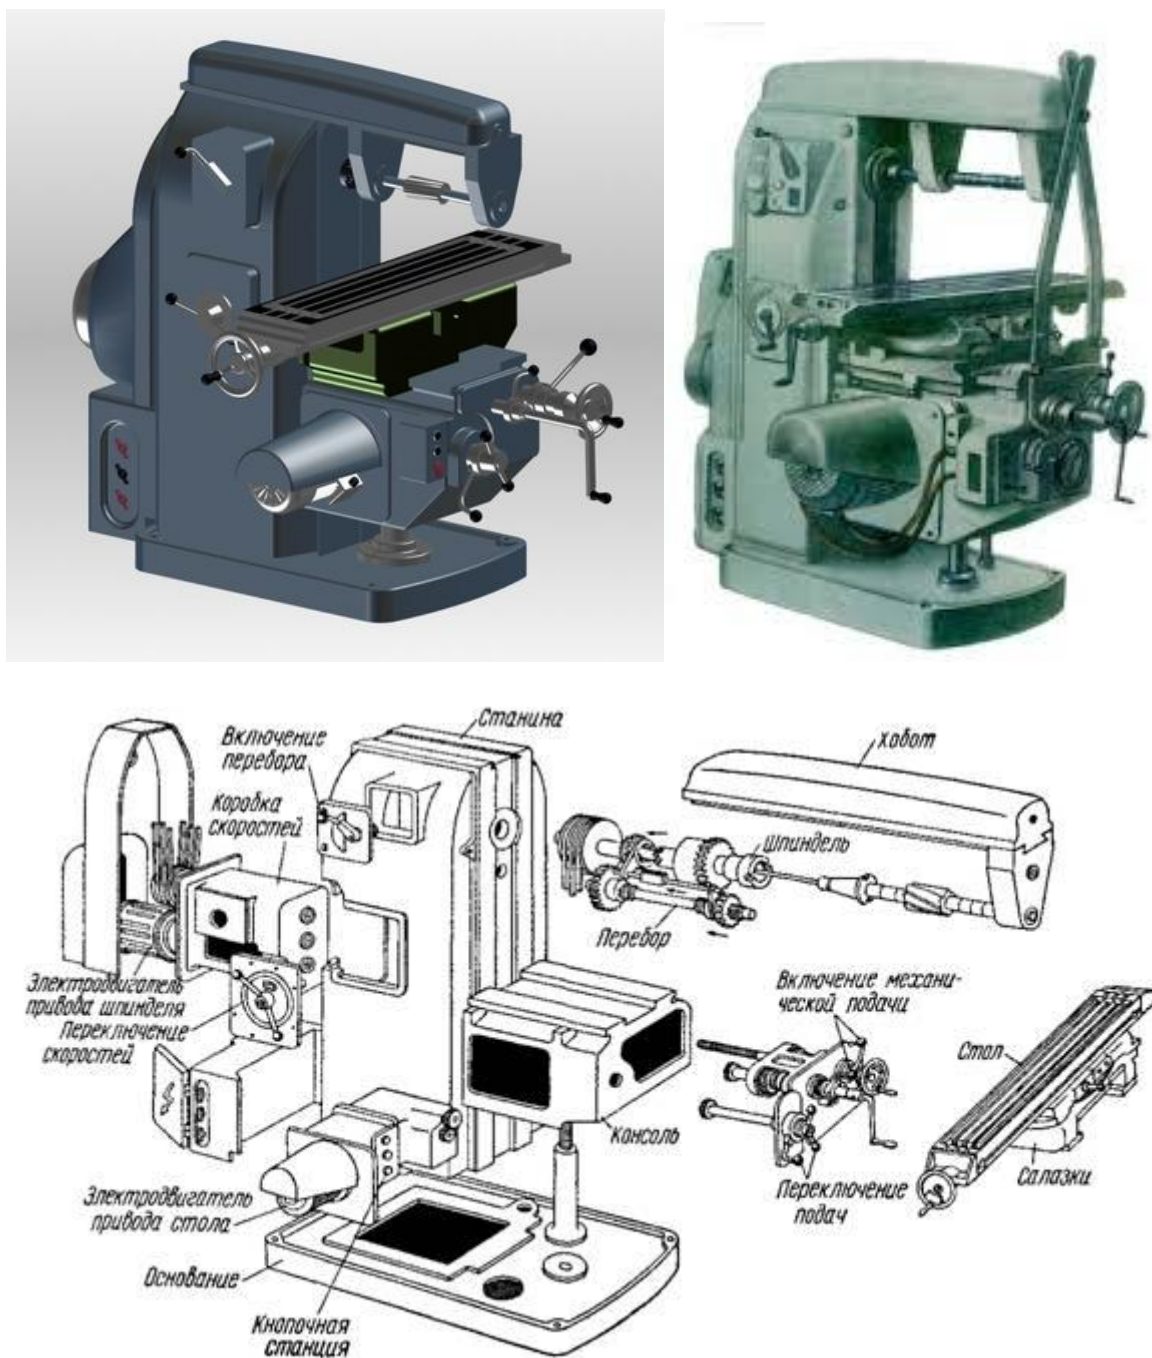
Горизонтально-фрезерный станок мод. 6Н81Г
